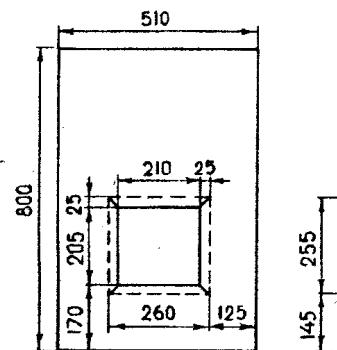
Верхний боковой облицовочный лист с отверстием для варочной
